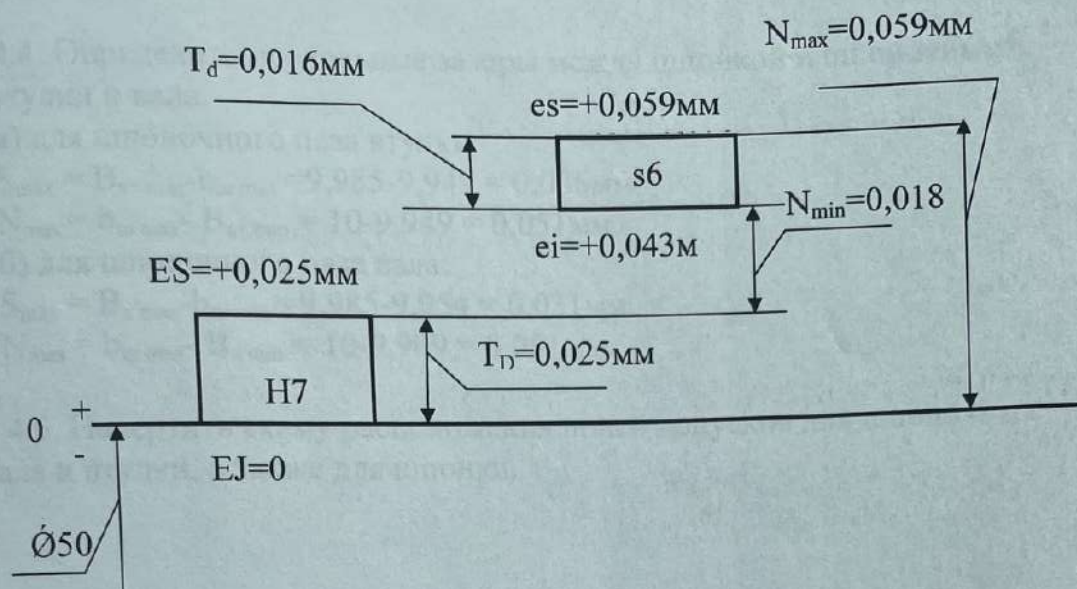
Схема расположения полей допусков для отверстия и вала.
